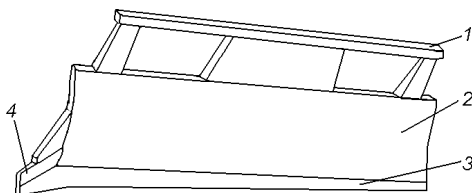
Однокорпусный кусторезный отвал: 1 – защитная конструкция; 2 – отвальная поверхность; 3 –режущая кромка; 4 – колун.
